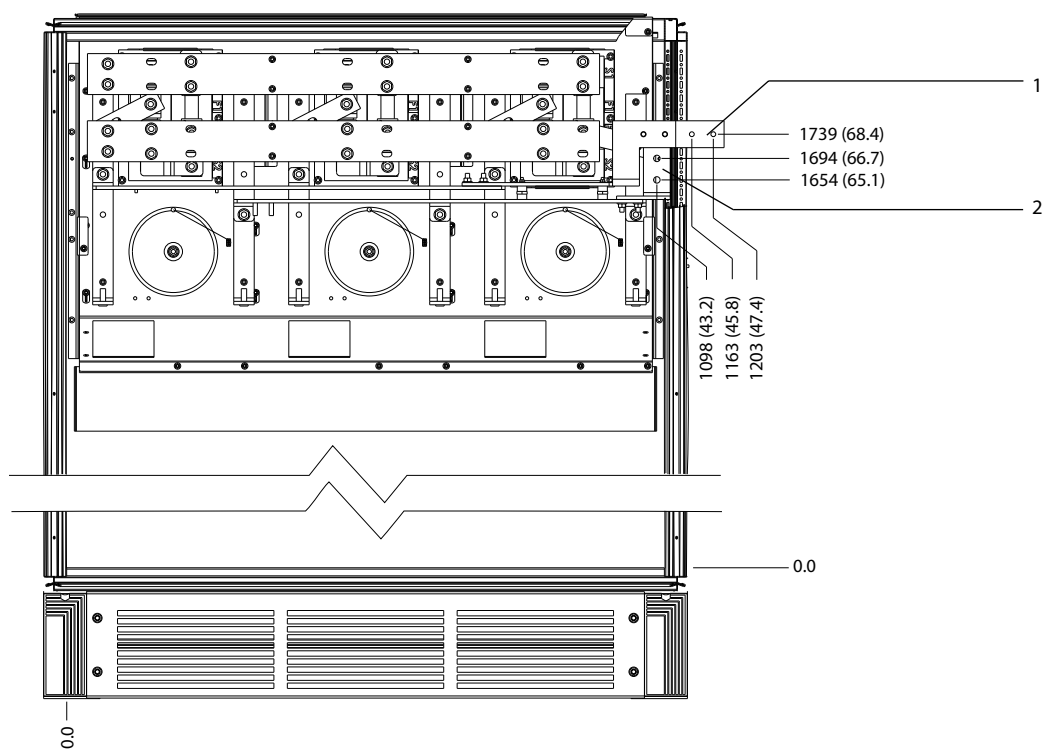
Размеры клемм для шкафа инвертора F2/F4, вид спереди
